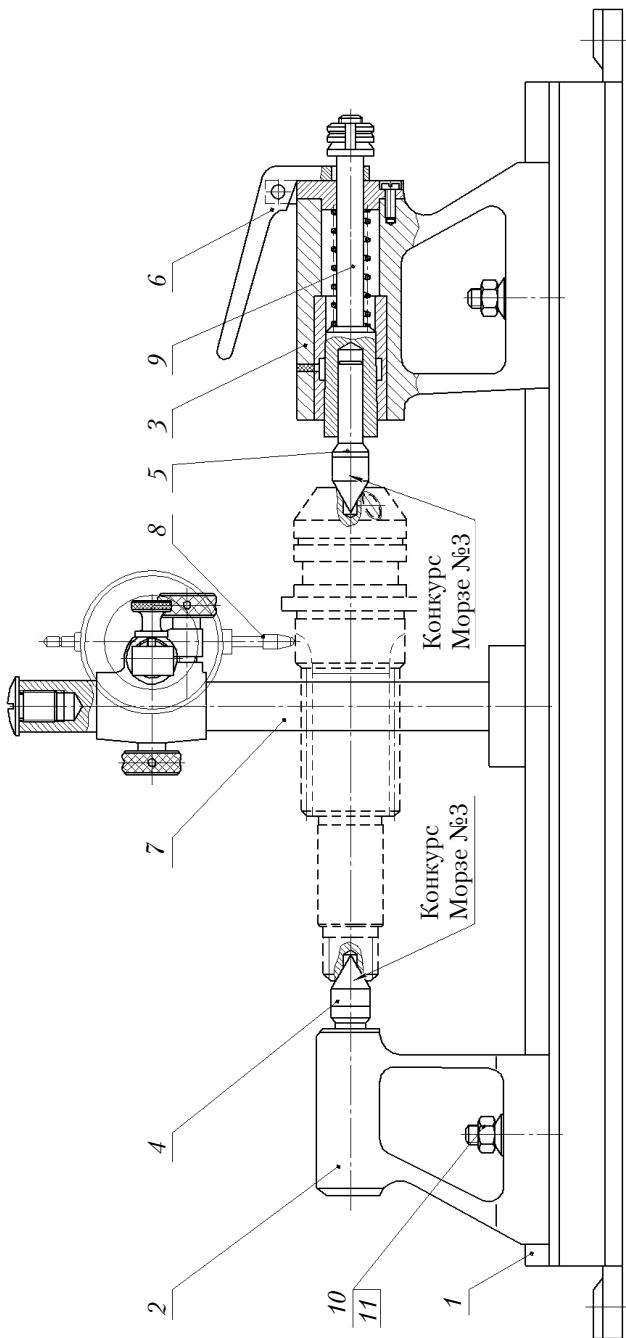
Приспособление для контроля радиального биения шеек вала-шестерни относительно оси детали
